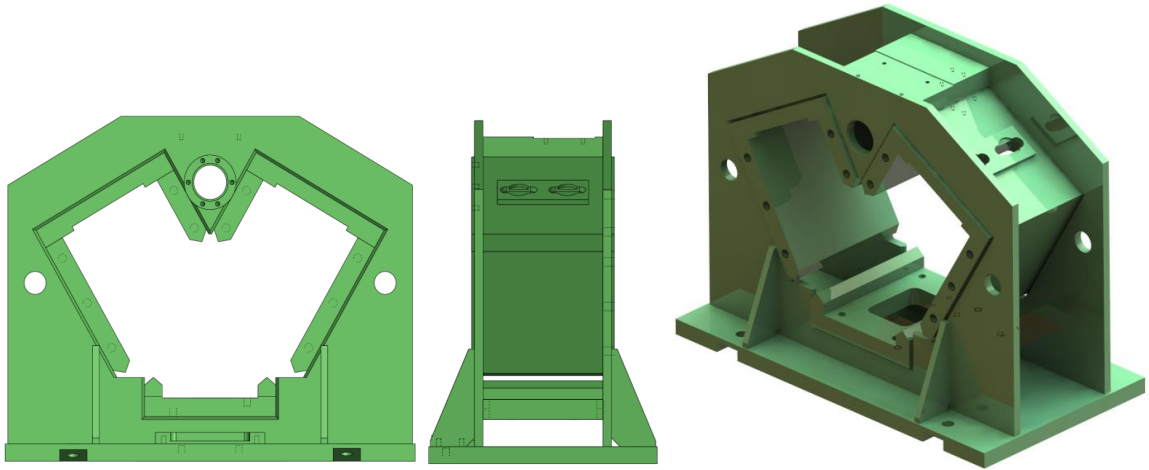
Общий вид станины клетки трехвалкового прошивного стана «30-80»
